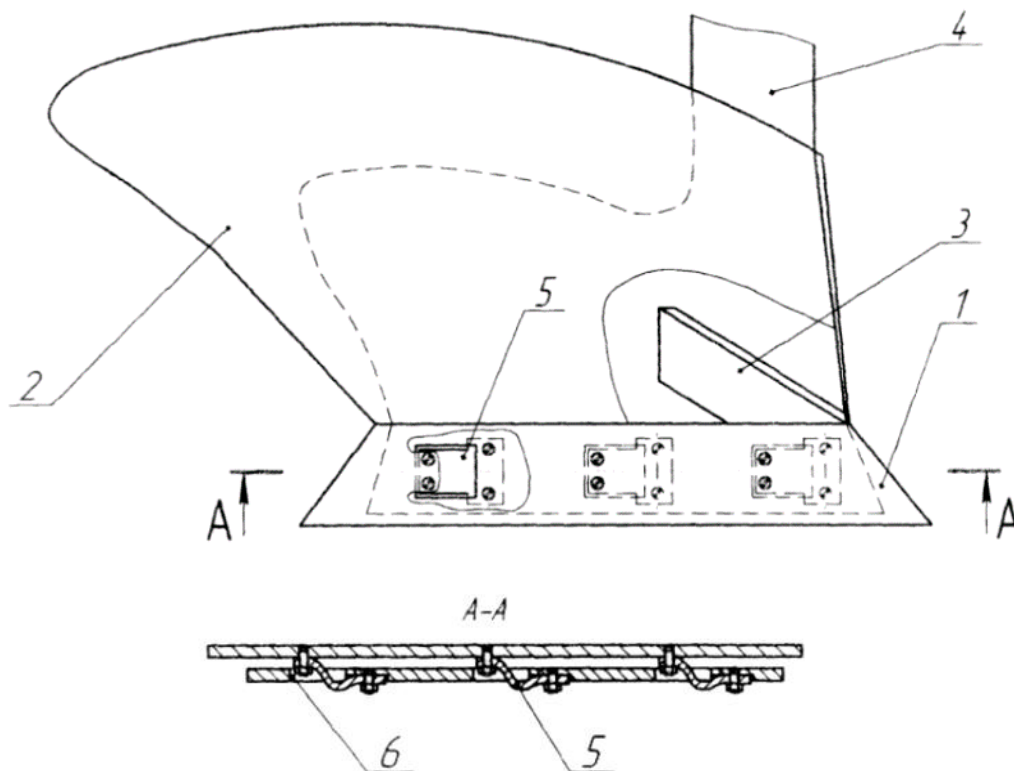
Корпус плуга з підпружиненим лемішем [105]
